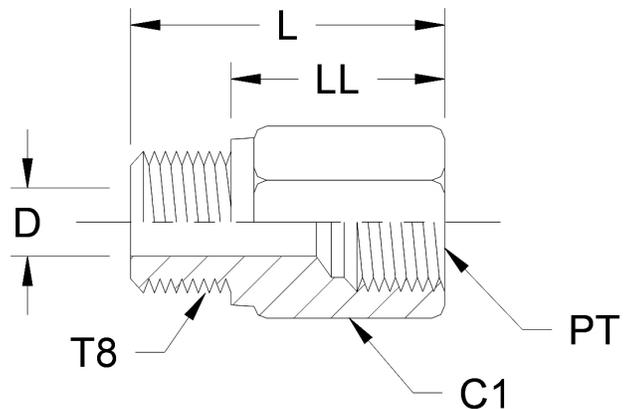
Diagrama dimensional del Adaptador de conversión - Métrica a NPTF
